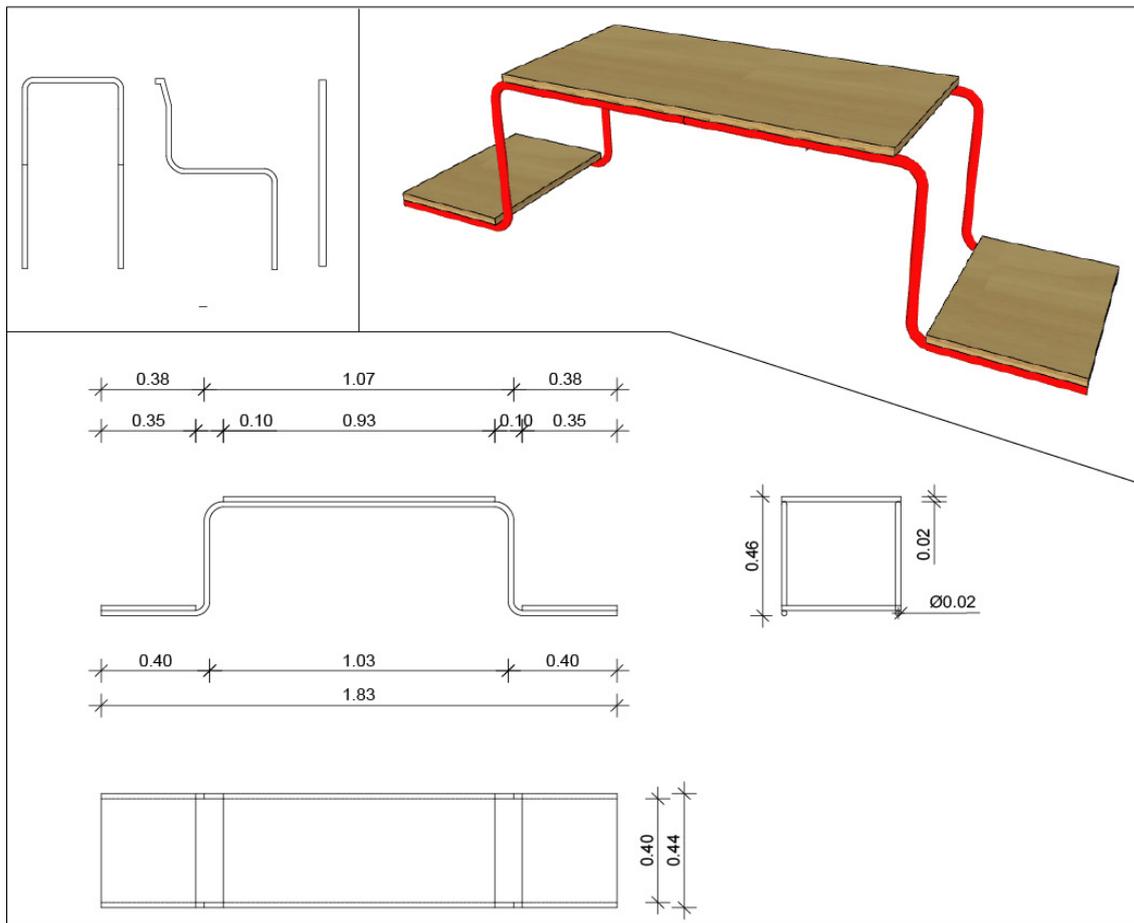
Desenho técnico Móvel 3. Fonte: Autor
